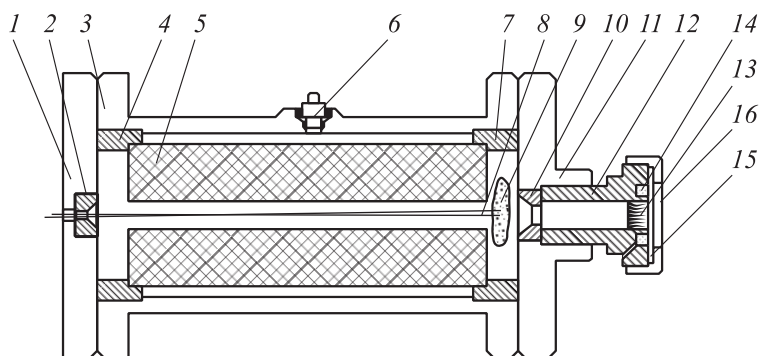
Схема модельного двигателя: 1 — передняя крышка; 2 — основное сопло; 3 — корпус камеры; 4 — переднее фиксирующее кольцо с зубцами; 5 — пороховая трубка; 6 — датчик давления; 7 — заднее фиксирующее кольцо с зубцами; 8 — воспламенитель МБ-2; 9 — навеска дымного пороха (ДРП); 10 — дополнительное сопло; 11 — задняя крышка; 12 — корпус вышибного устройства; 13 — пробка; 14 — кольцевая проточка с ДРП и МБ-2; 15 — мембрана; 16 — крышка вышибного устройства
